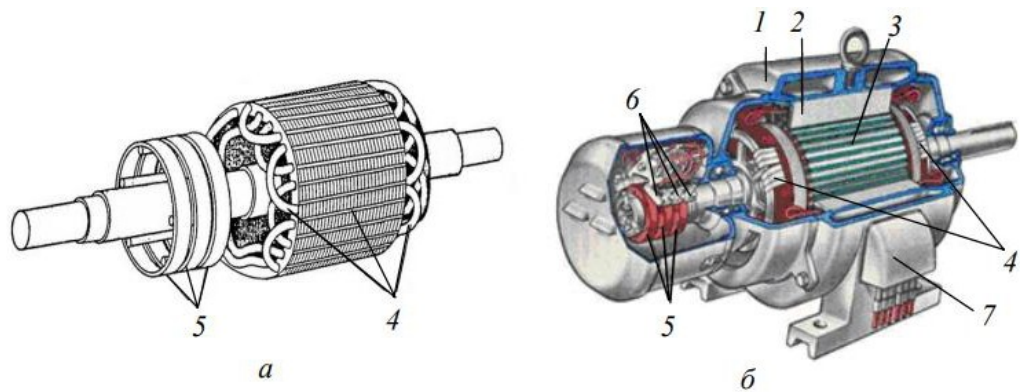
Фазний ротора (а) та асинхронної машини з фазним ротором в розрізі (б): 1 – станина; 2 - сердечник статора, 3 - сердечник ротора; 4 - обмотка ротора; 5 - контактні кільця; 6 – щітки; 7 - клемна коробка
